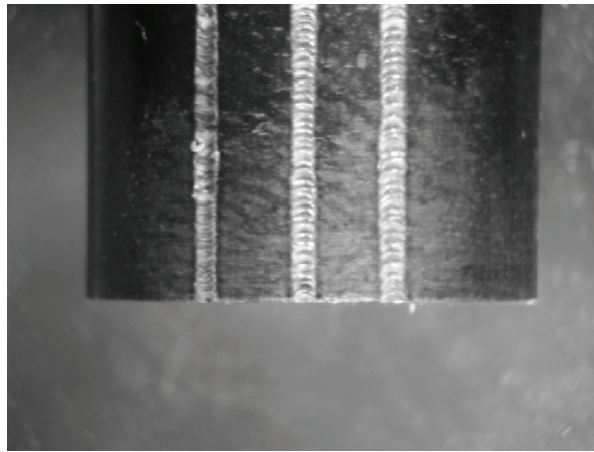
Вид заготовки после лазерной обработки и обрезки
